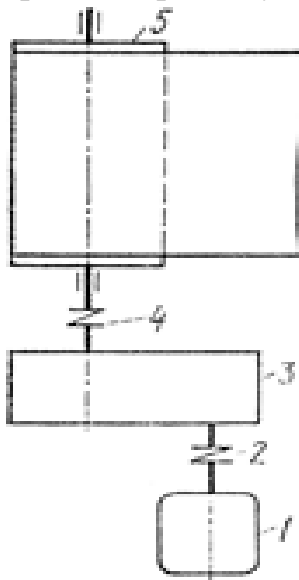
Схема привода ленточного конвейера: 1 – двигатель; 2, 4 – муфты; 3 – редуктор; 5 – приводной барабан
